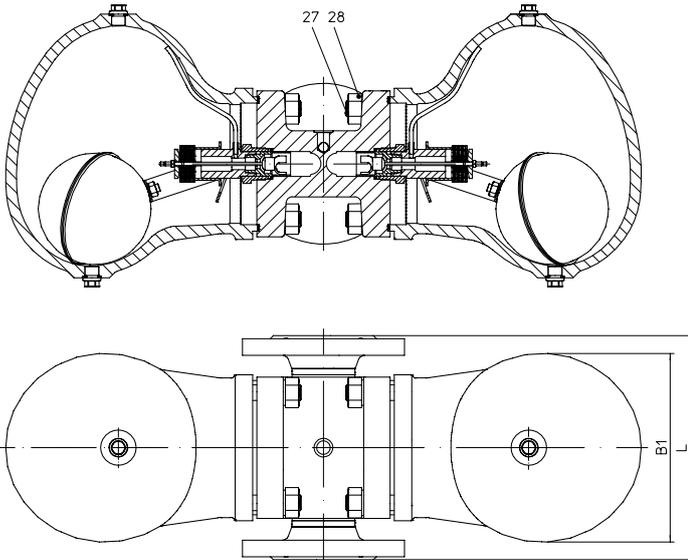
1 mit Flanschen - horizontale Einbaulage
